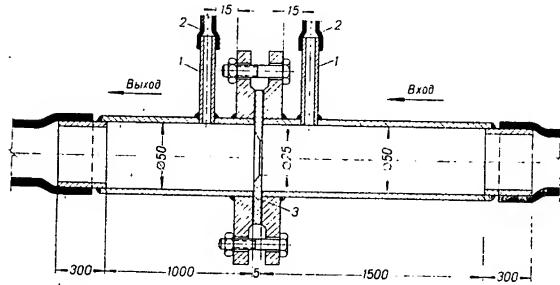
Приспособление для замеров расхода воздуха и газа: 1—ниппели для подсоединения дифманометра; 2—резиновые трубы для подключения; 3—диафрагма.
